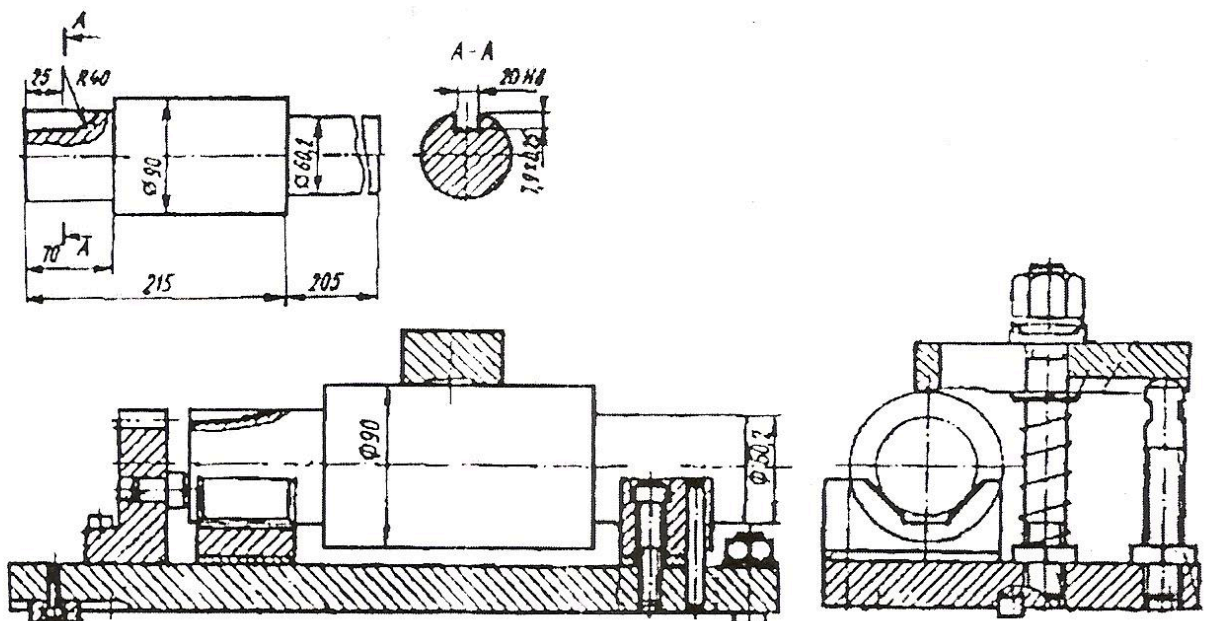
Закрепление в приспособлении детали типа «вал»
